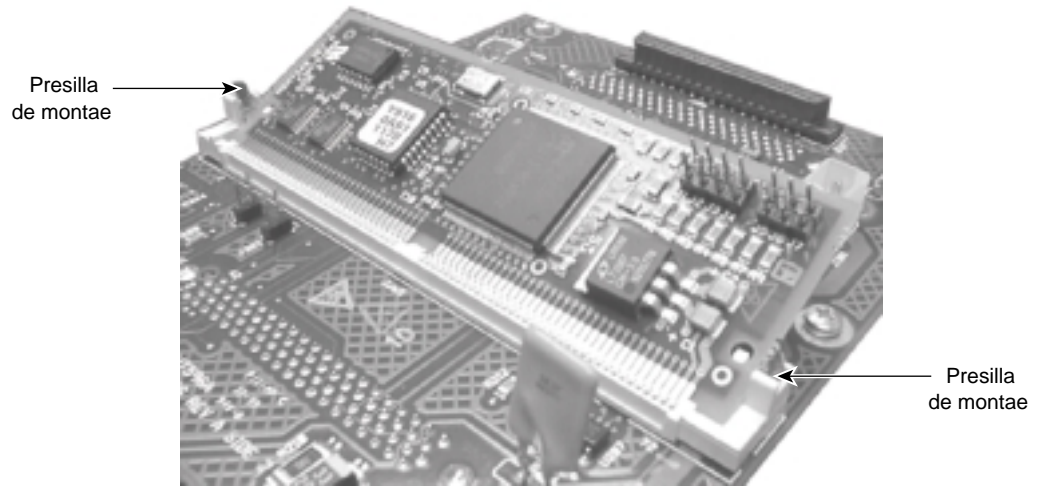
Presillas de montaje de la tarjeta SAF-TE
